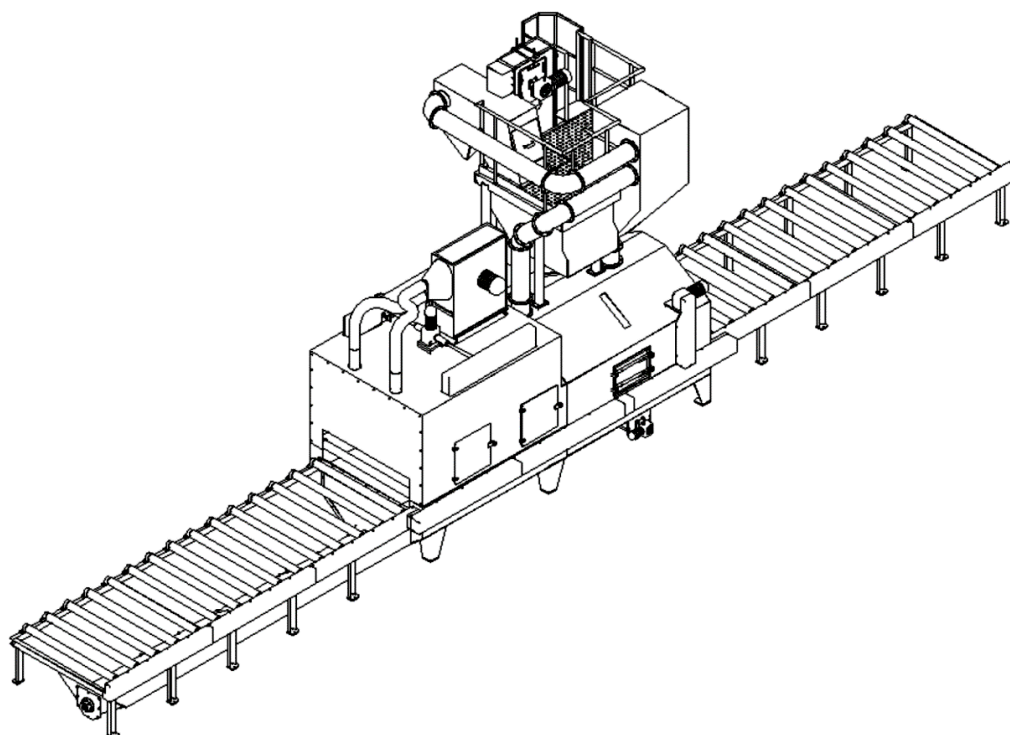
Станок для дробеметной очистки листового металла R 1600 x 500 «GOSTOLTST»
